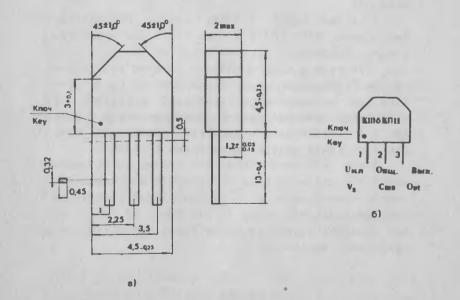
Микросхема К1116КП11: а - корпус; б - цоколевка.
